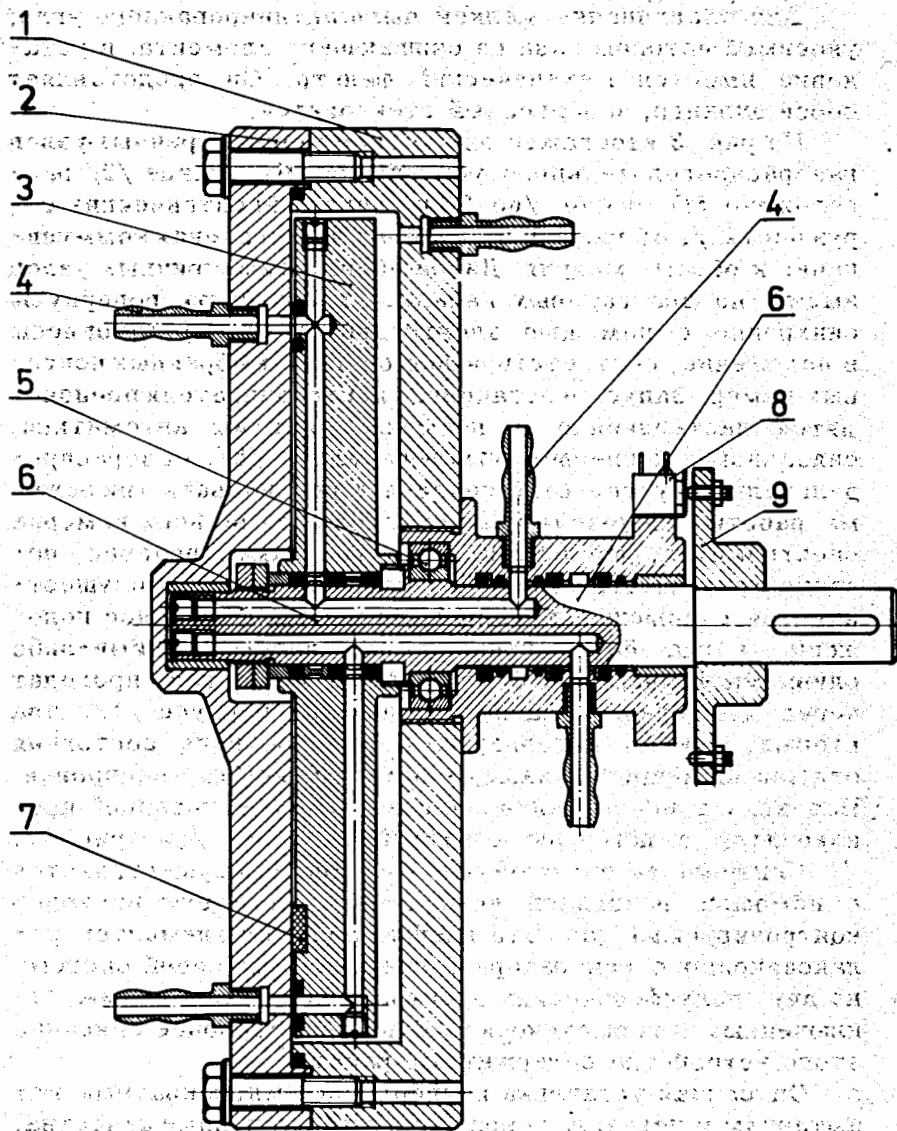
Узел распределительного устройства. 1 - корпус; 2, 9 - фланцы, 3 - диск; 4 - оливка; 5 - подшипник; 6 - вал; 7 - вкладыш; 8 - концевой выключатель.
